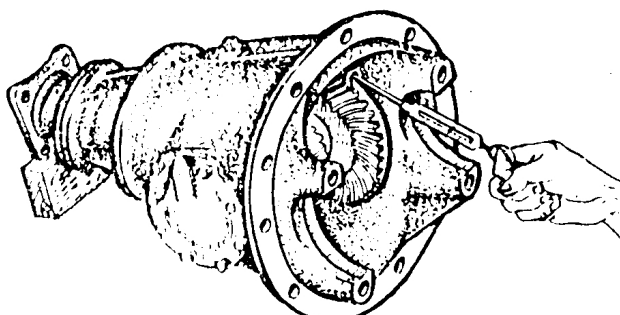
Проверка затяжки подшипников вала ведущей цилиндрической шестерни редуктора заднего моста автомобиля ЗИЛ
